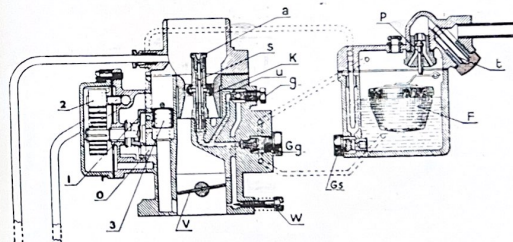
Corte del carburador SOLEX 28 IBT.
